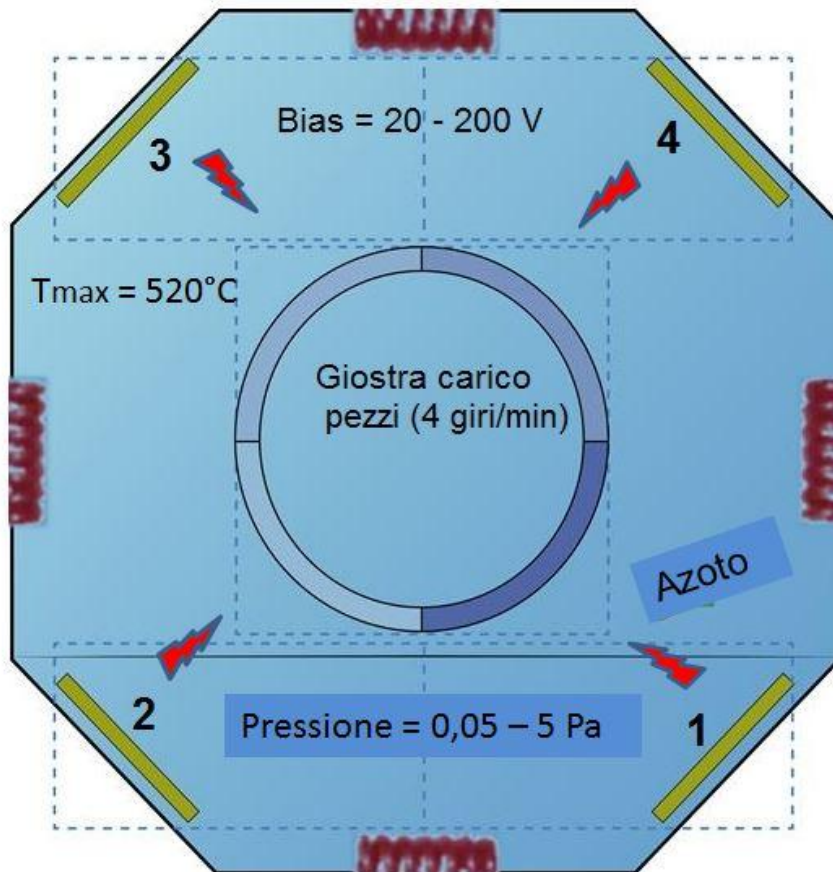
Disposizione schematica della camera di ricopertura PVD
